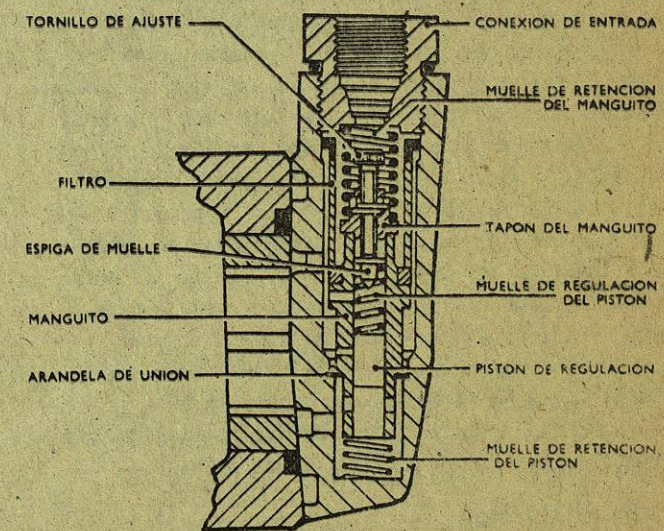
Placa de extremo con ajustador de presión de trasiego atornillado
